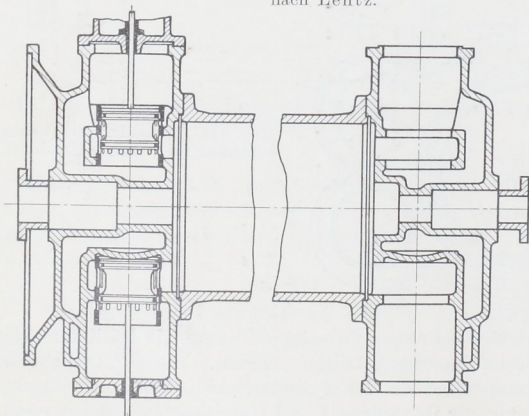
Zylinder mit Kolbenventilsteuerung.
